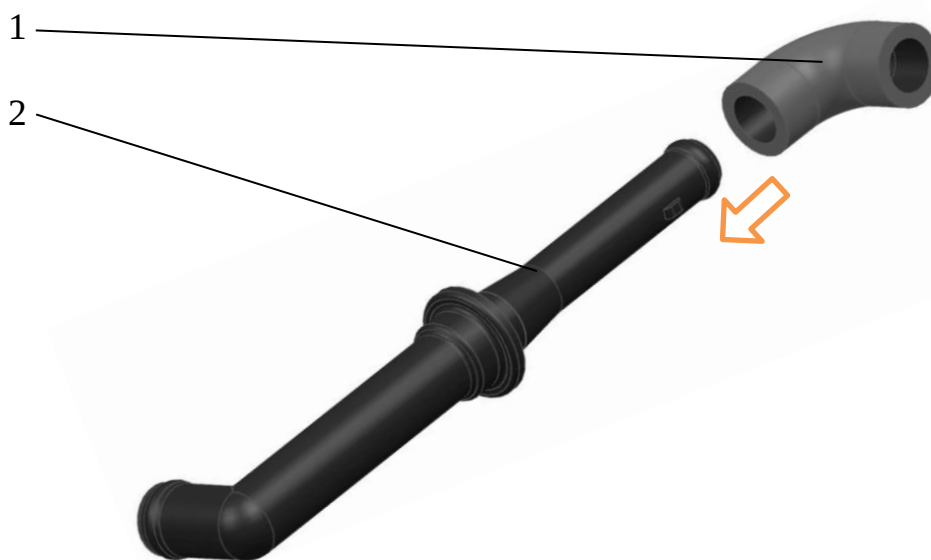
Подсборка трубки вентиляции с обратным клапаном с угловым шлангом:
